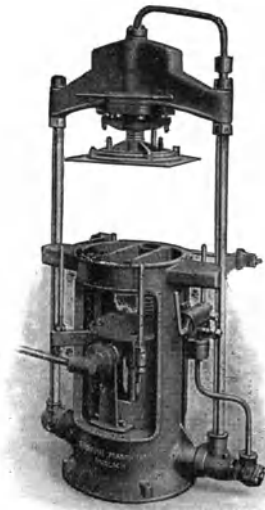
Stiftabhebemaschine mit Druckwasserbetrieb.
